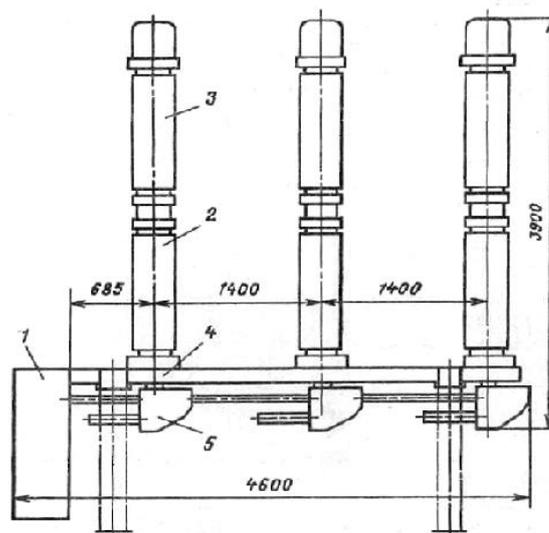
Габаритные размеры выключателя ВМТ-110
